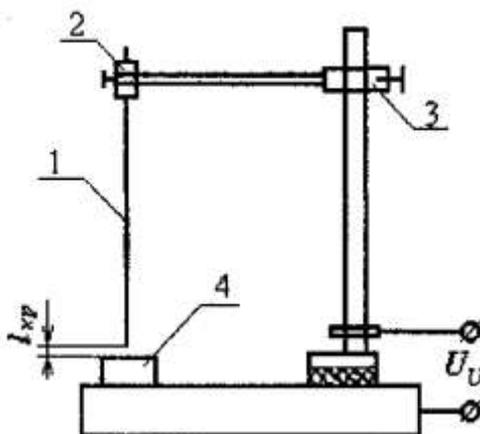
Схема для исследования критической длины сварочной дуги, $L_{кр}$
